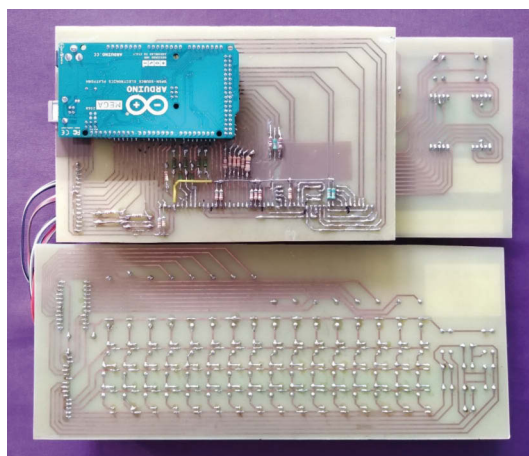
Vue côté soudures (et des résistances qui avaient été oubliées...)
